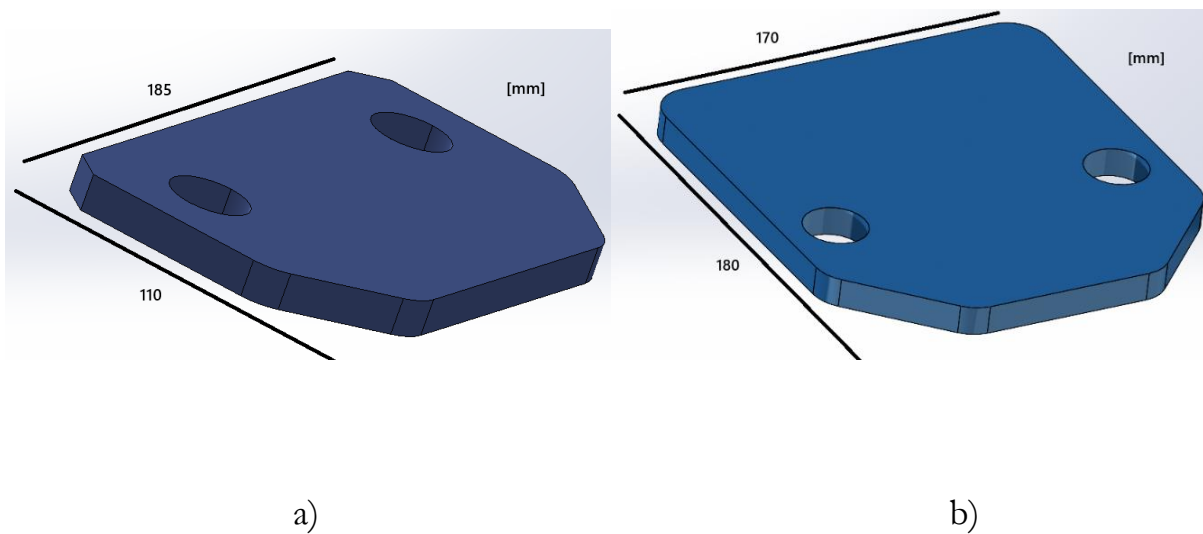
Dimensões da testa: a) WH30; b) desenhada.
